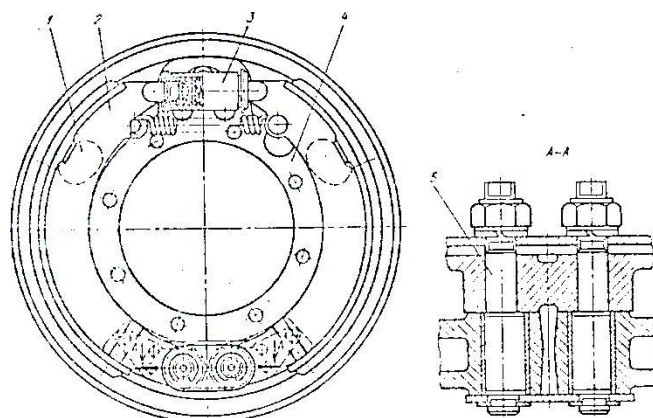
Тормоз барабанного типа: 1 – эксцентрик; 2 – колодка; 3 – гидроцилиндр; 4 – тормозной щит; 5 – опорные пальцы;
